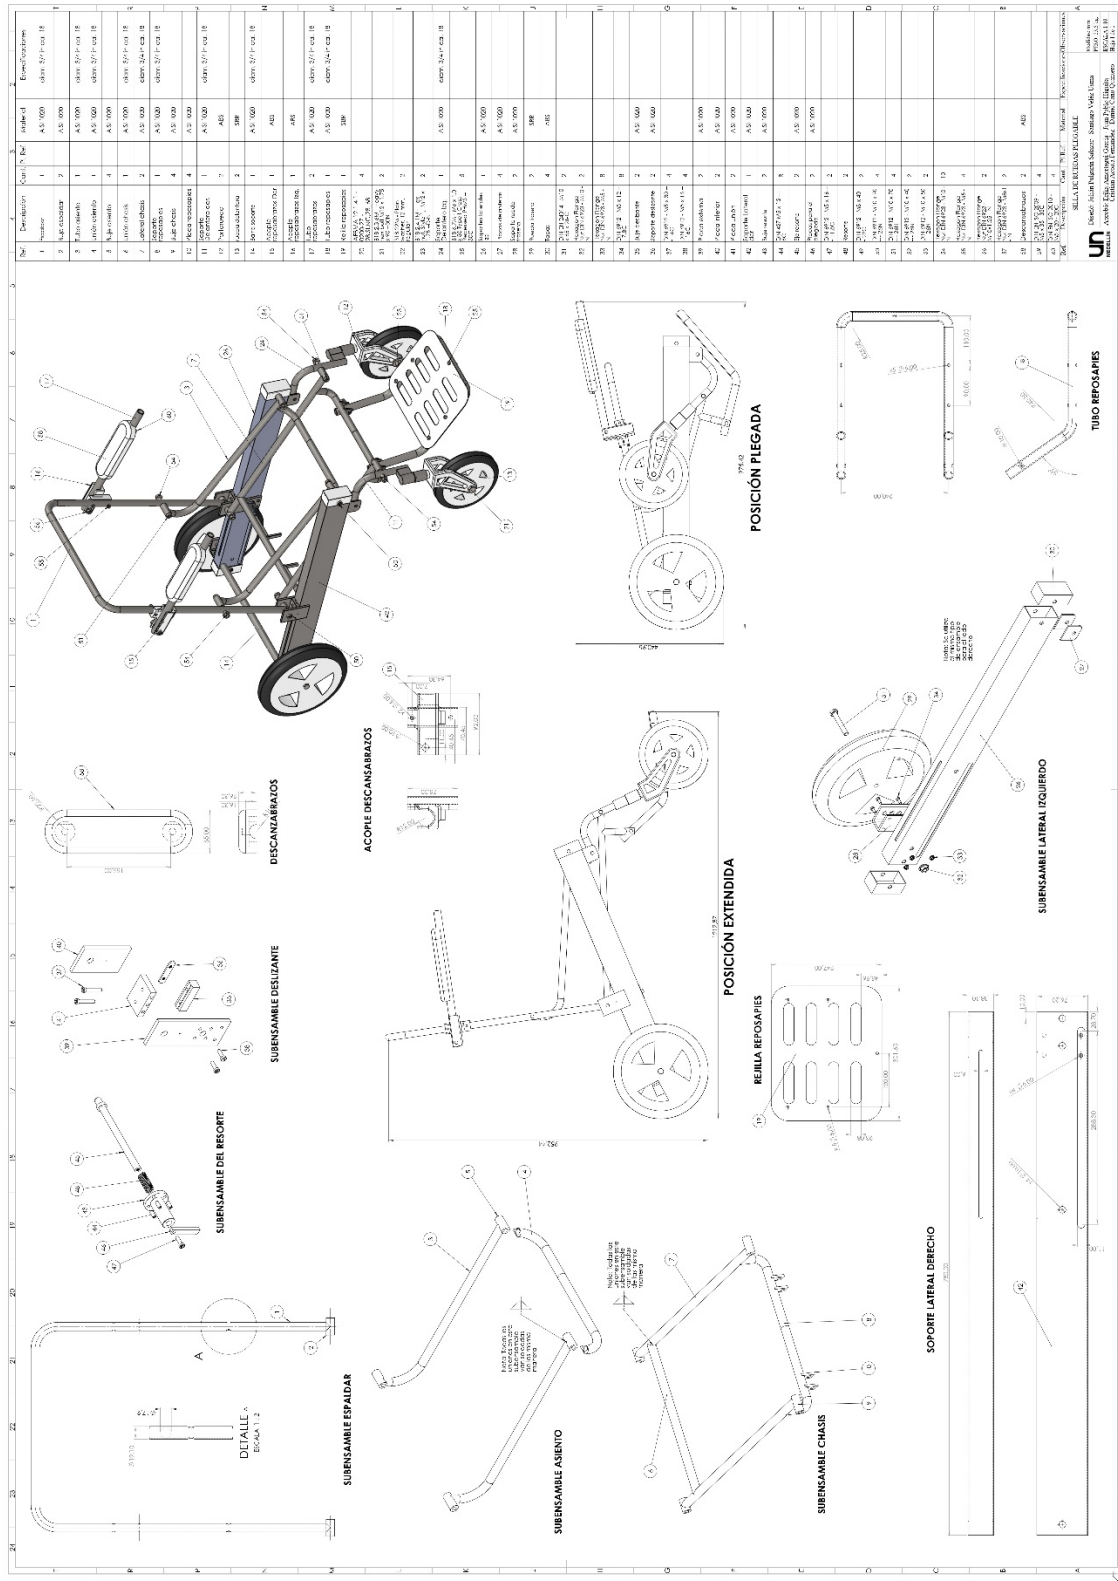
Plano de ensamblaje de la silla de ruedas diseñada.
